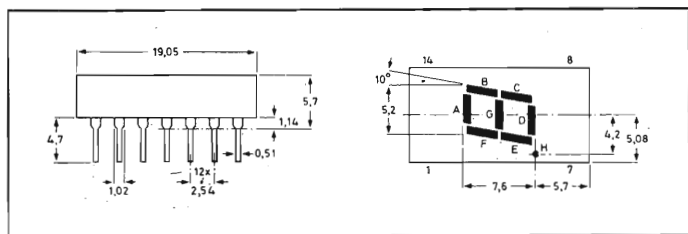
Dimensioni dell'indicatore a 7 segmenti CQY 81.
